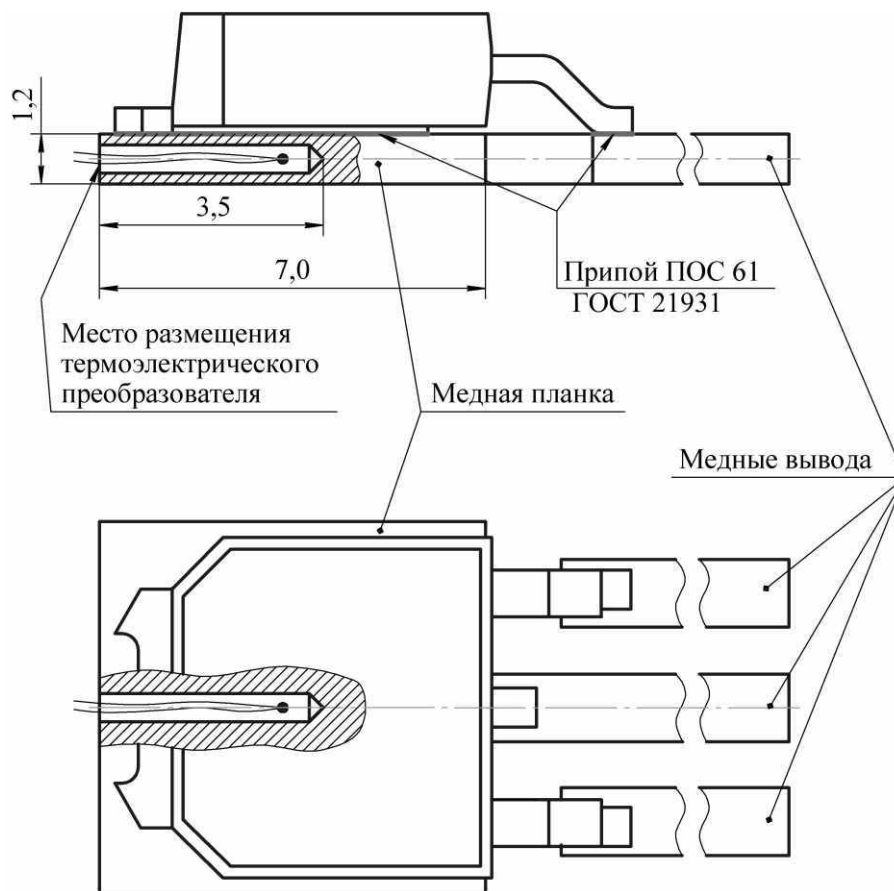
Место размещения термоэлектрического преобразователя для контроля температуры корпуса сборок в корпусе КТ-89
